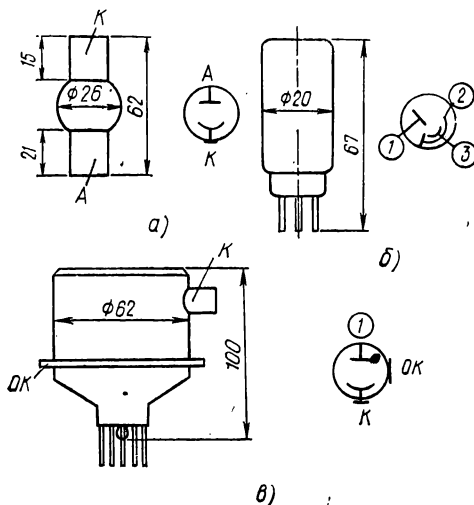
Габаритные чертежи и цоколевка вакуумных фотоэлементов:
